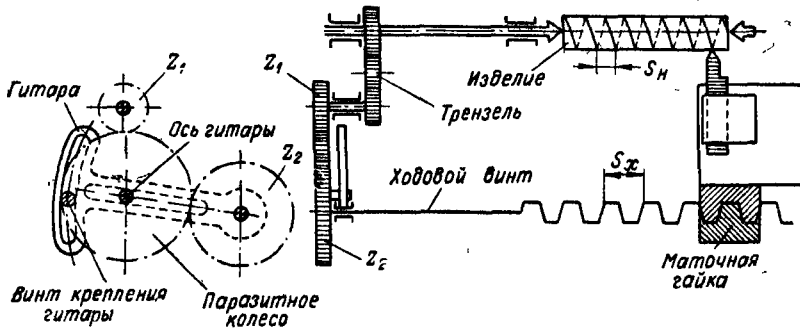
Схема к настройке токарного станка на нарезание резьбы.
